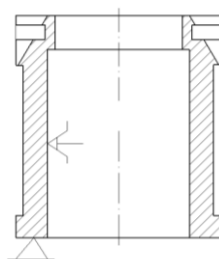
Схема базування на рперації фрезерування косих пазів
